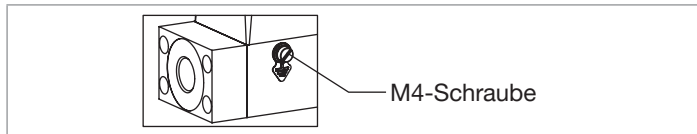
Position der M4-Schraube für den Anschluss des Funktionserdungskabels
